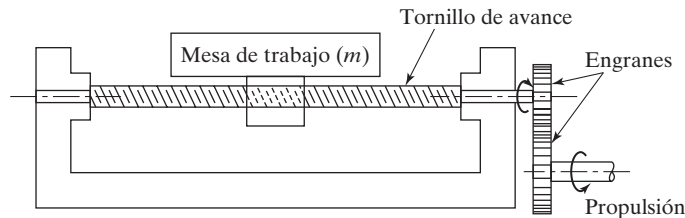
Movimiento de una mesa de trabajo mediante un tornillo de avance en una máquina herramienta.
